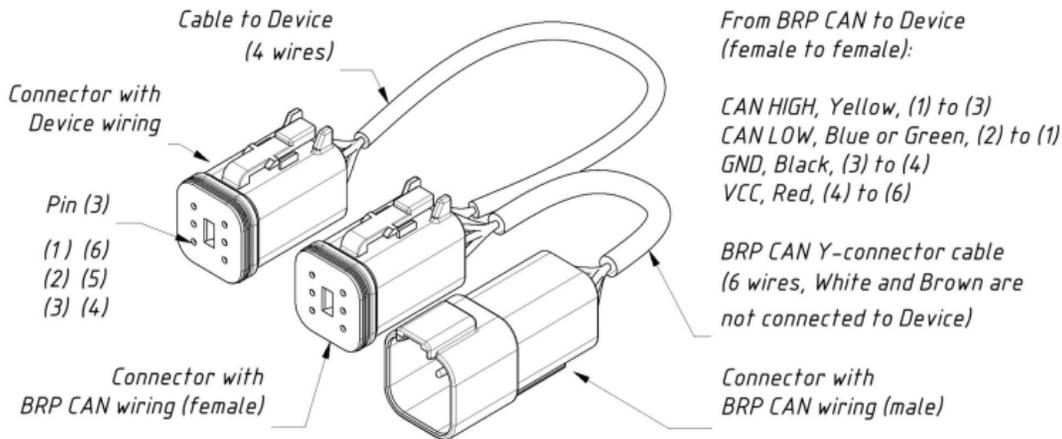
Adapterkabel für BRP-Diagnosestecker
